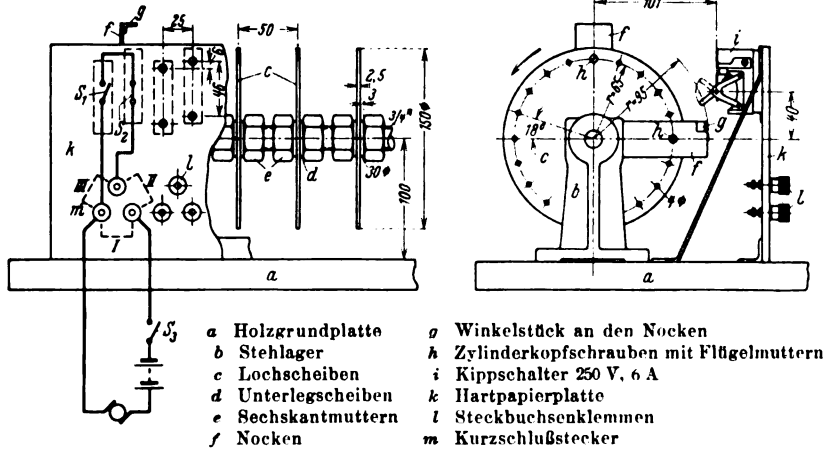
Ausführungszeichnung der Schaltmaschine für Versuchszwecke.
